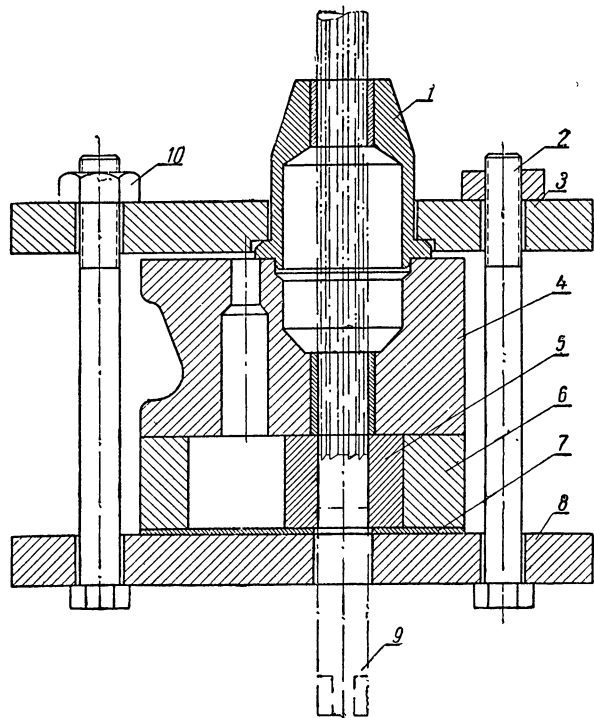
Совместная развертка втулок валика подкачивающей помпы:
